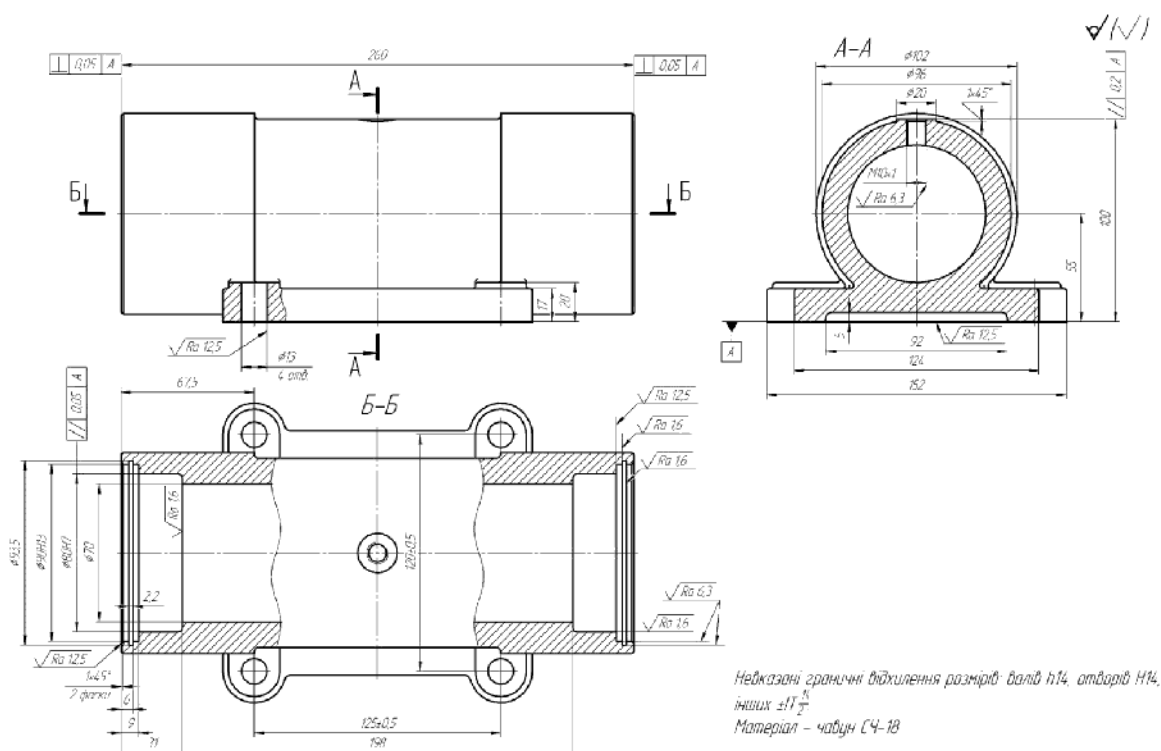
Ескіз маршруту механічної обробки деталі "Корпус"
